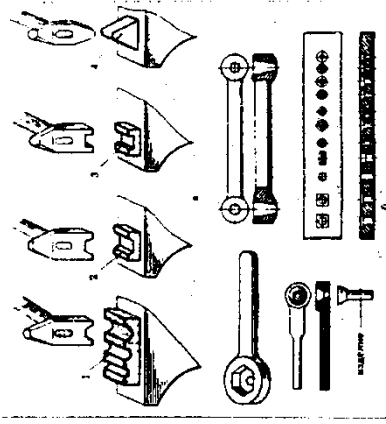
Парный подкладной инструмент: а — обжимки (1—3) и подбойка (4); б — приспособления для высадки гвоздей, болтов, заклепок
